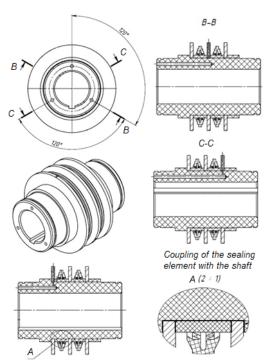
Стандартный блок контактных колец для асинхронных электродвигателей с фазным ротором
